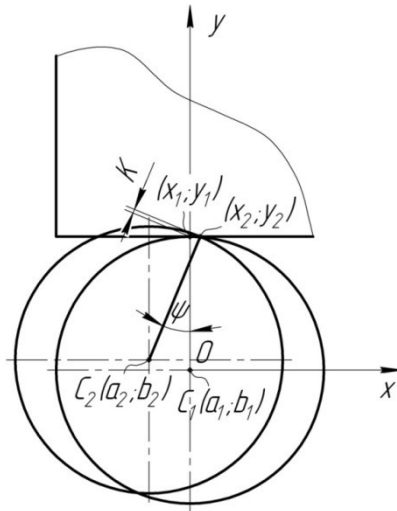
Схематичное изображение двух последовательных положений торцовой фрезы
